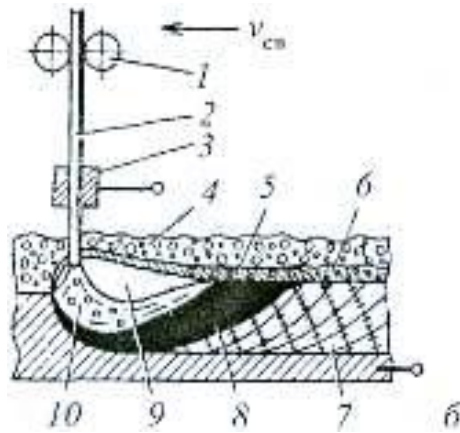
Схема процесса автоматической дуговой сварки под флюсом
